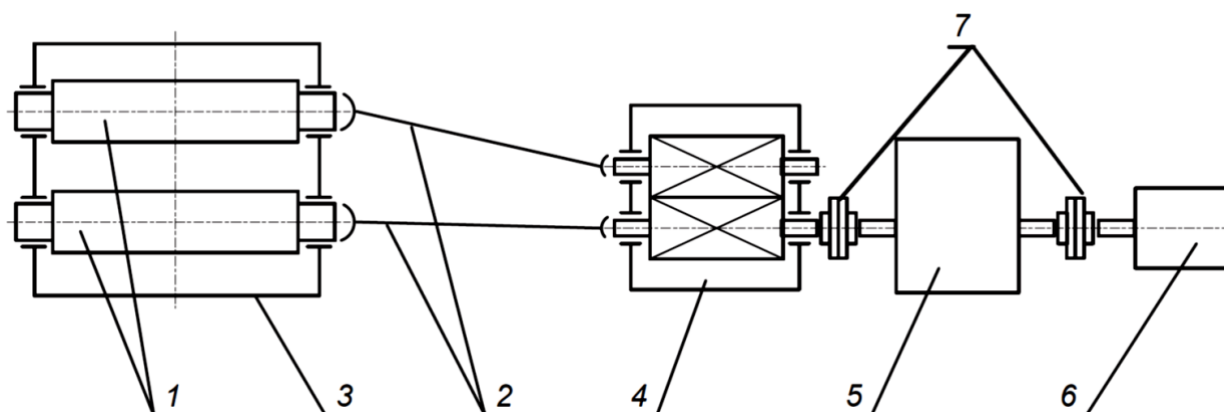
Схема прокатной клетки: 1 – валки; 2 – шпиндели; 3 – станина; 4 – шестеренная клетка; 5 – редуктор; 6 – двигатель; 4 – моторная и коренная муфты
